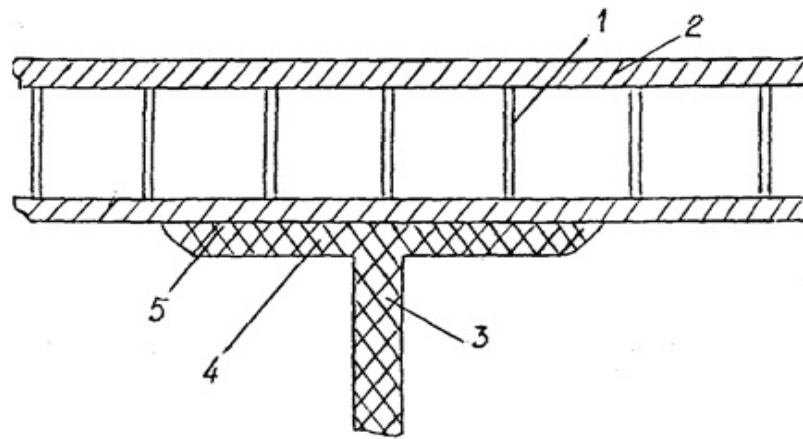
Типові дефекти конструкції з КМ: 1- розшарування трубчатого заповнювача обшивки; 2 – розшарування зовнішньої та внутрішньої обшивки; 3 – розшарування стінки лонжерона; 5 – розшарування поясу лонжерона від внутрішньої обшивки
